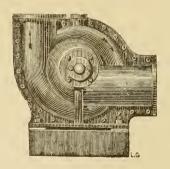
Pompe centrifuge Dumont, vue de côté.
